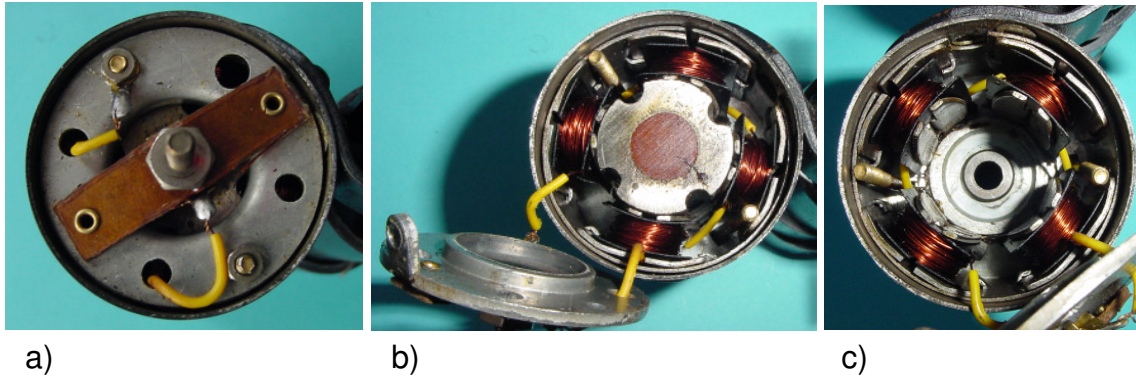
Baugruppen: a) Grundplatte, b) Läufer mit Anker, c) Anker
